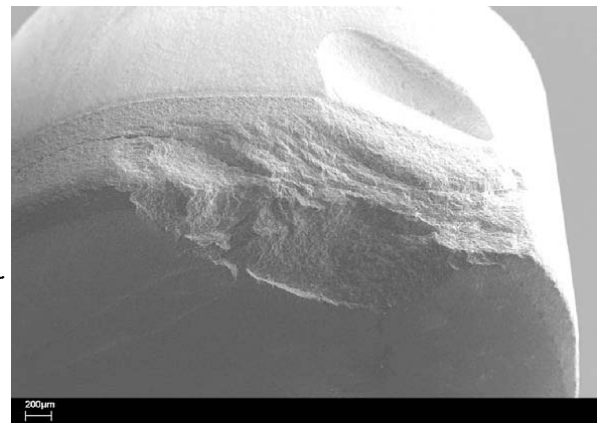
Grobe Ausbrüche an einem PKD-Probekörper [65]
